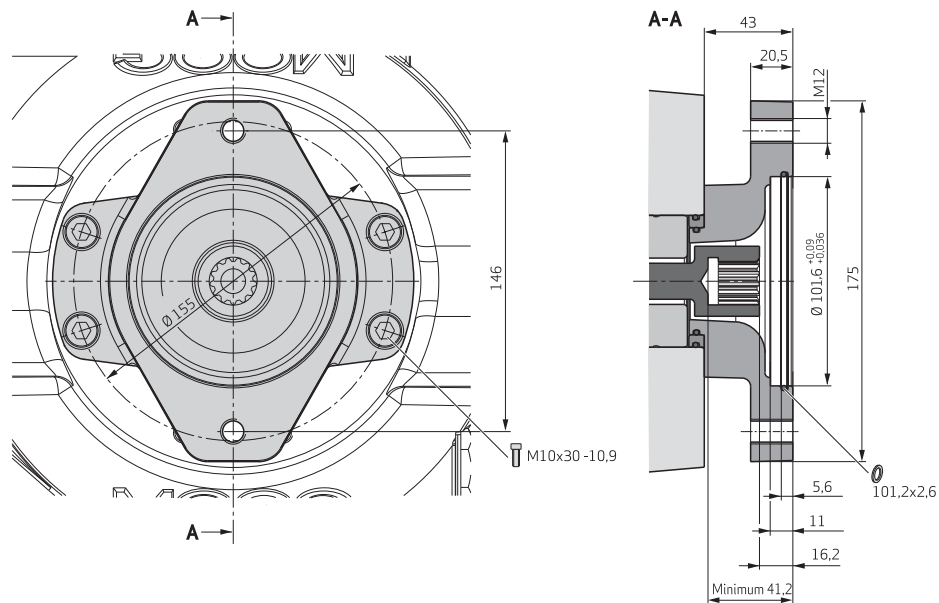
Adapterflansch SAE-B mit 13-zahniger Welle
